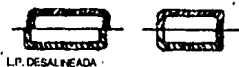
Desalineamiento del molde. (Ref. 2).
